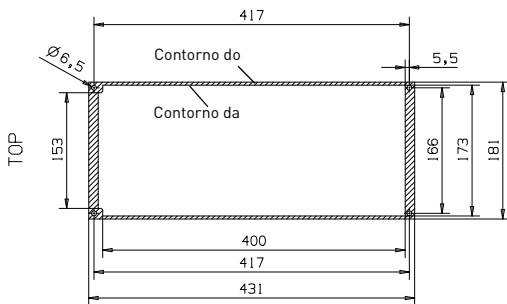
Dimensões do recorte para montagem com flange do MR4 ao MR6 (unidade: mm)
